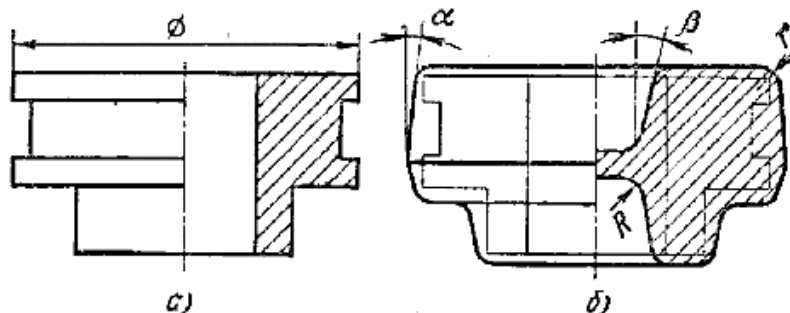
Пример составления чертежа поковки: а – деталь; б – поковка
